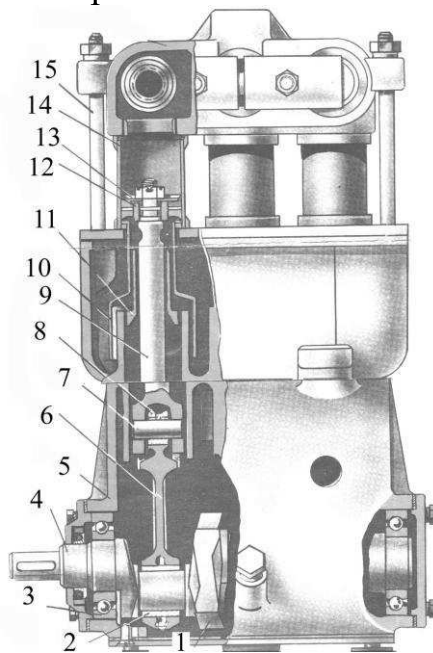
Поршневой жидкостный насос УН-41000: 1 – лопасть разбрызгиватель масла; 2 – подшипник скольжения (вкладыш); 3 – шарикоподшипник; 4 – коленчатый вал; 5 – корпус насоса; 6 – шатун; 7 – палец; 8 – втулка шатуна; 9 – шток ползуна; 10 – предохранительный колпак; 11 – втулка штока; 12 – втулка поршня; 13 – манжета; 14 – цилиндр насоса; 15 – шпилька с клапанной коробкой
